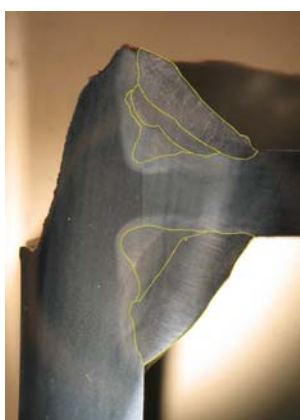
Reconstituição dos cordões de soldadura.
